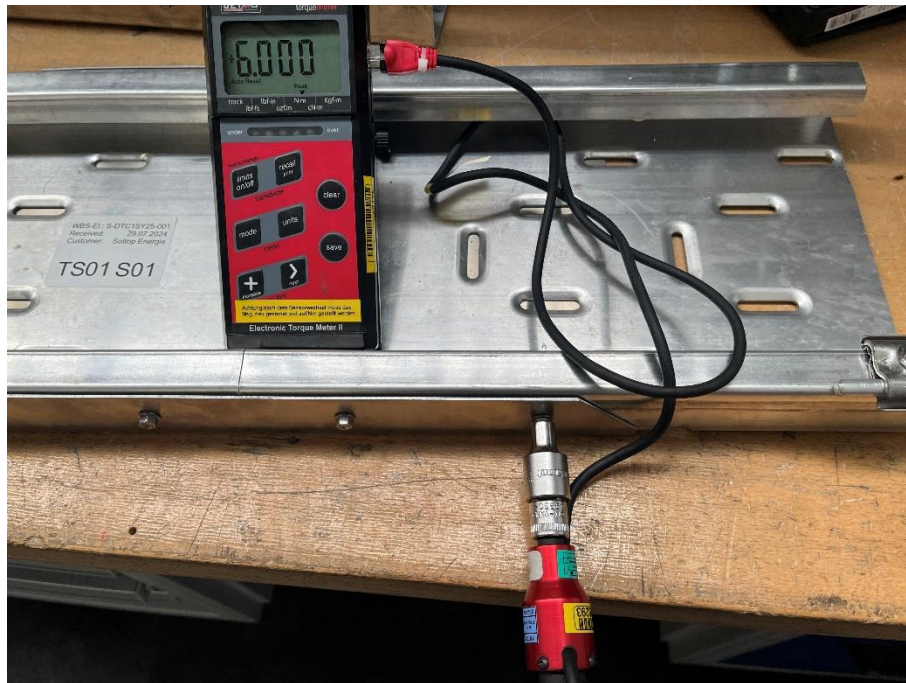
Drehmomentmessung – Bohrschraube 1 – exemplarisch für die Bohrschrauben.
